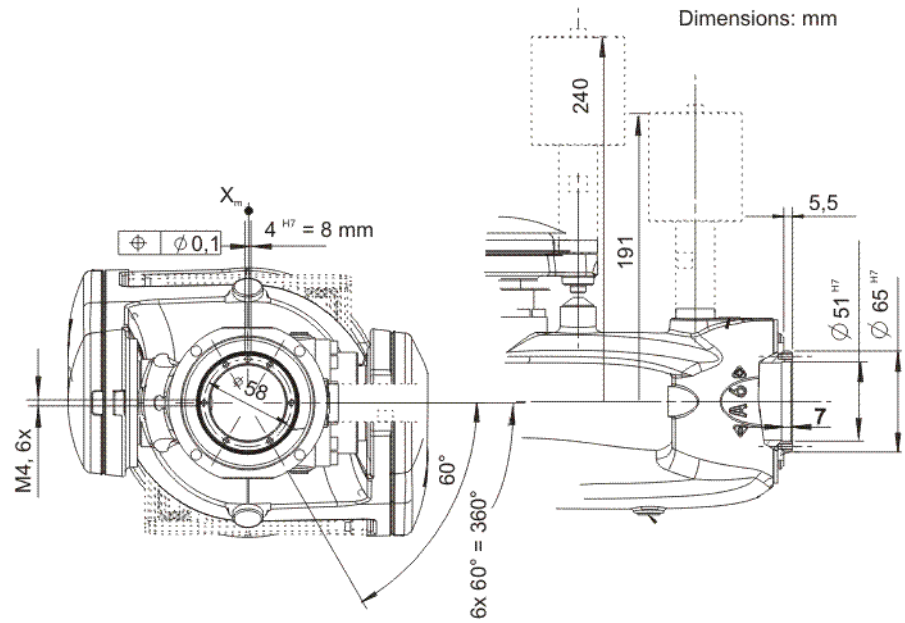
Bride de fixation KR 16 L8 arc HW
